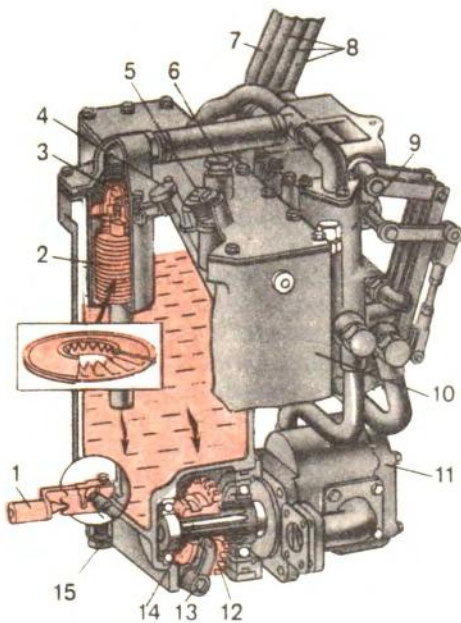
Корпус гидроагрегатов трактора МТЗ-80:
